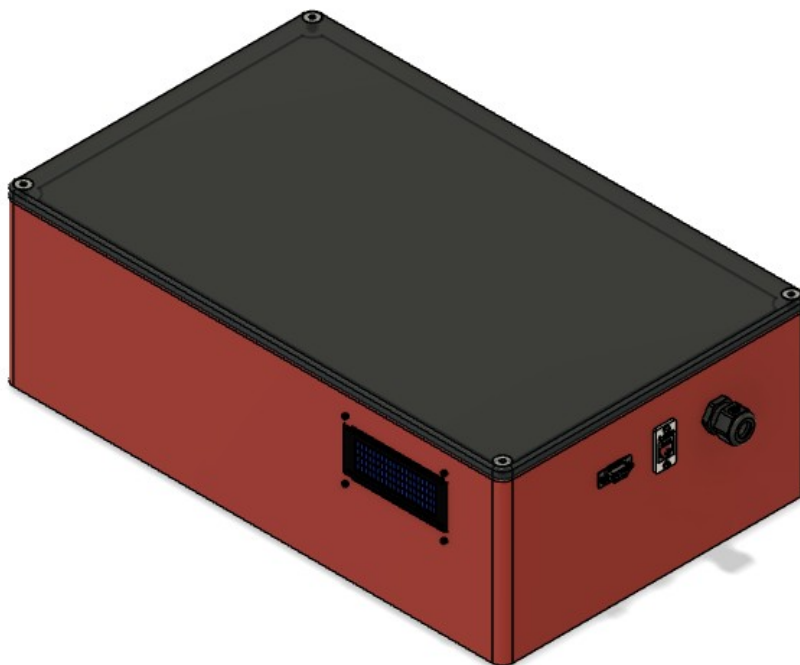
Imagen Frontal del Diseño en 3D del Prototipo
